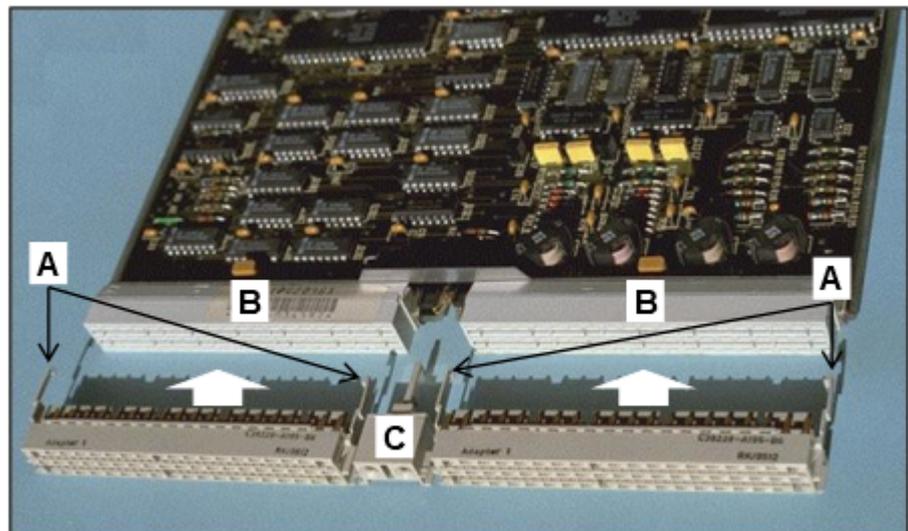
Montage des SIVAPAC-SIPAC-Baugruppenadapters
